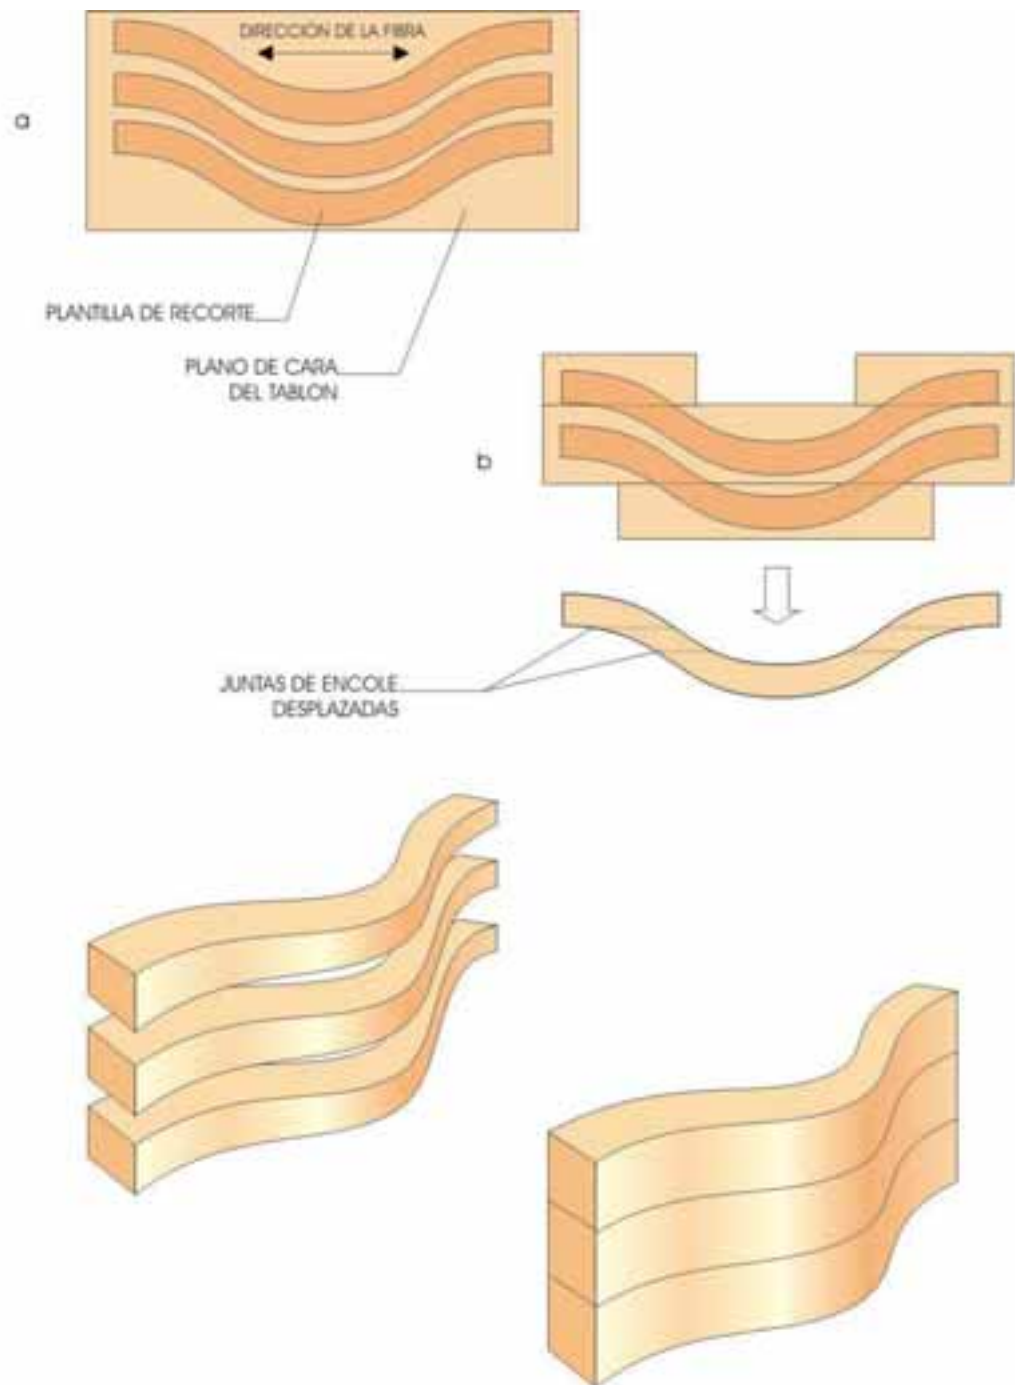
Despiece para encole paralelo de formato horizontal.
